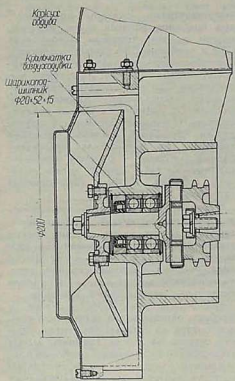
Привод воздушодувки и кожух обдува для двигателя ИЖ-56.
